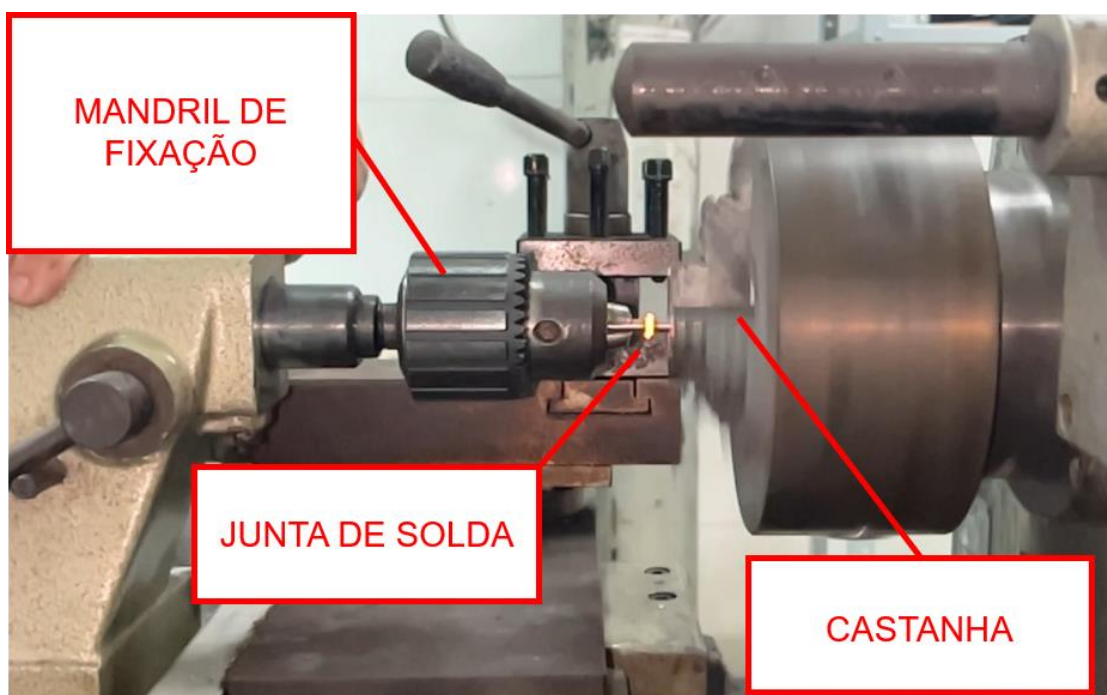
Aquecimento localizado provocado pela fricção durante a soldagem. Indicado como junta de solda na imagem.
